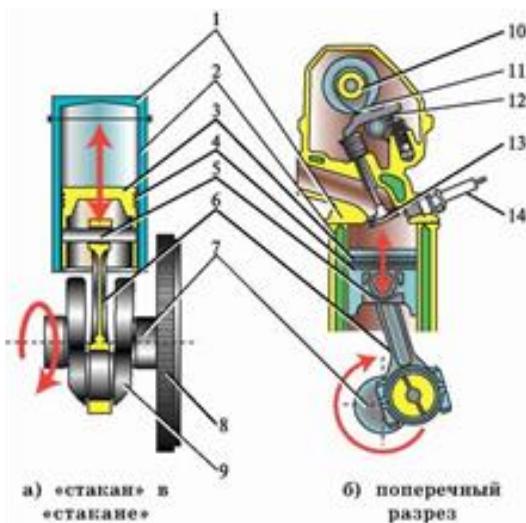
Одноцилиндровый бензиновый двигатель внутреннего сгорания: 1 – головка цилиндра; 2 – цилиндр; 3 – поршень; 4 – поршневые кольца; 5 – поршневой палец; 6 – шатун; 7 – коленчатый вал; 8 – маховик; 9 – кривошип; 10 – распределительный вал; 11 – кулачок распределительного вала; 12 – рычаг; 13 – впускной клапан; 14 – свеча зажигания
